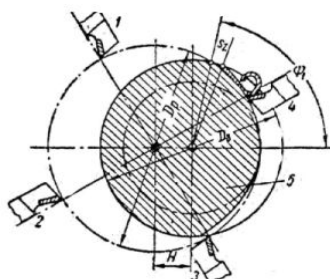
Схема обработки с применением продольной подачи (1-4-резцы резцовой головки; 5- обрабатываемая деталь).
